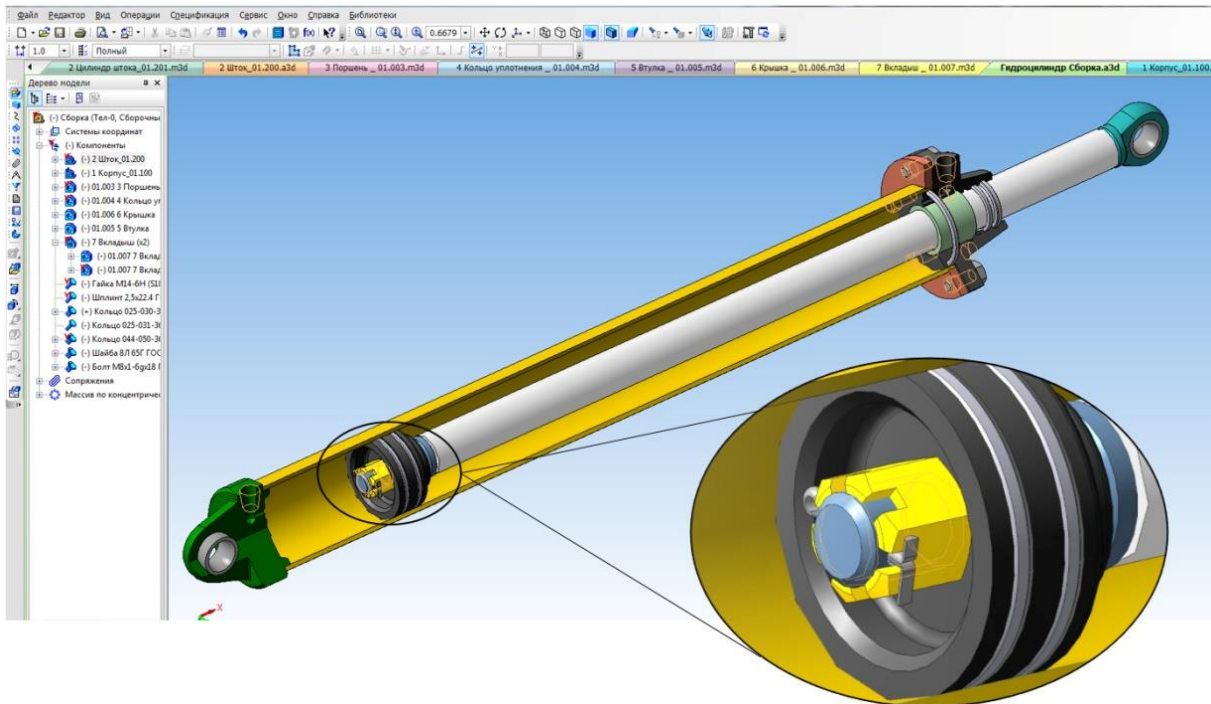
3D-модель гидроцилиндра подъемника
